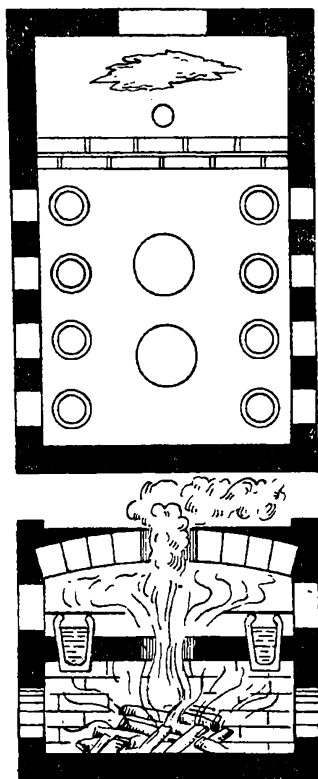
План и поперечный разрез стекловаренной печи, описанной Феофилом
